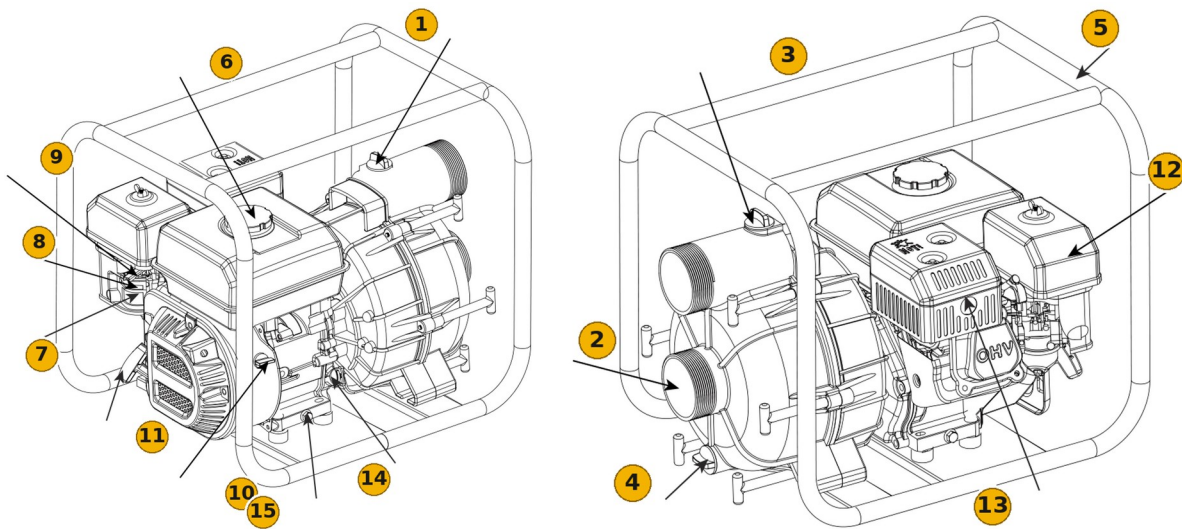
Motobombas SEMITRASH: vista do lado do motor e do lado da bomba
